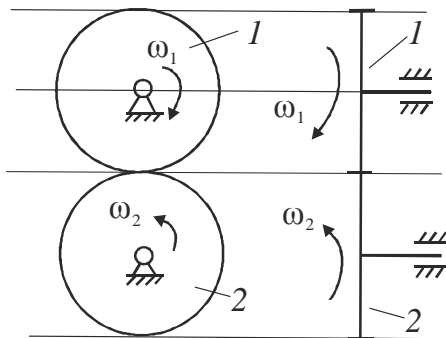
Изображение на кинематической схеме зубчатых колес
